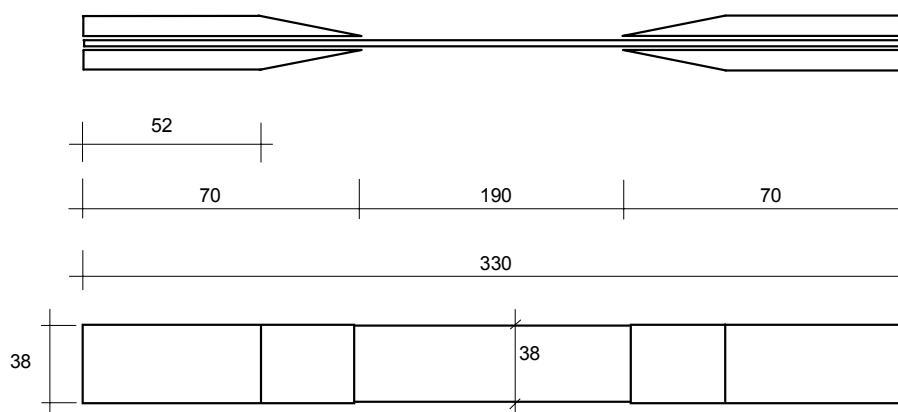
Dimensões dos corpos de prova do laminado com fibra de carbono (em mm)
